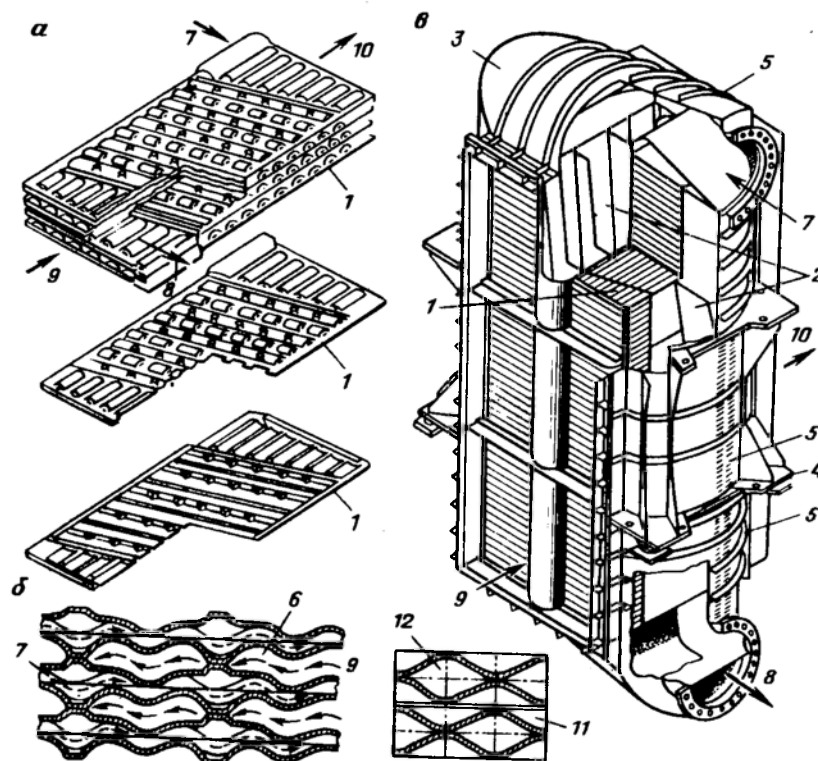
Пластиновый регенератор установок ГТК-10 и ГТ-700-12М НЗЛ:
